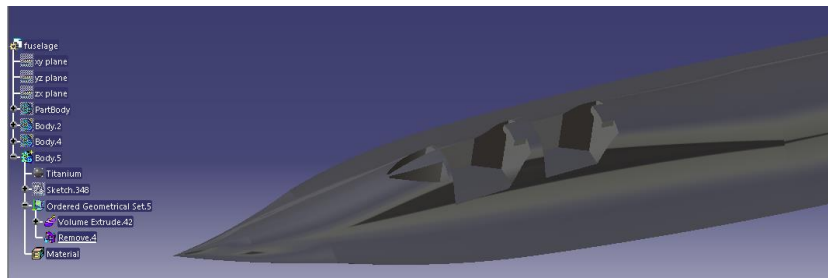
Diseño final del fuselaje del Lockheed SR-71
